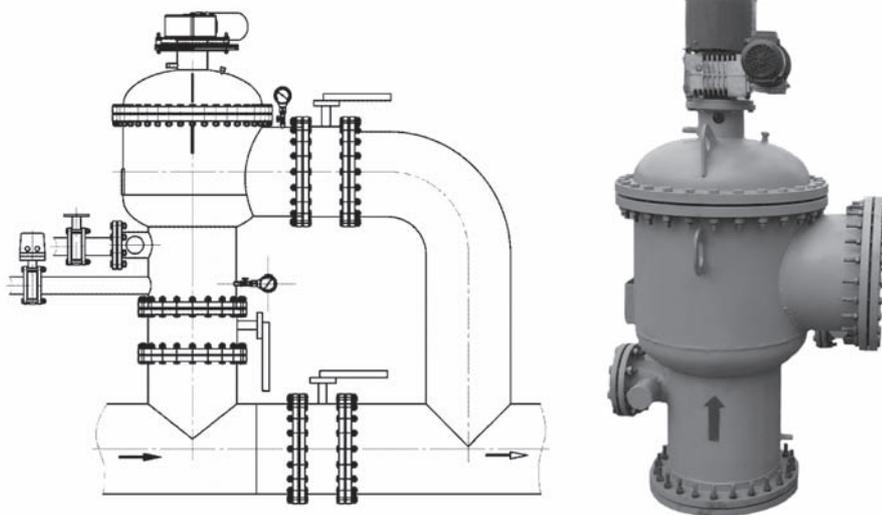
Монтажная схема и внешний вид фильтра типа ФСЦ
